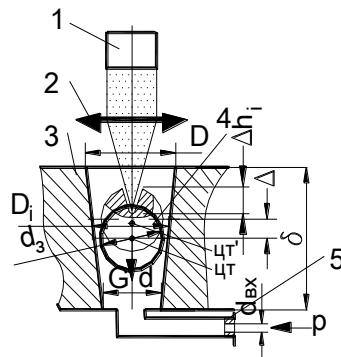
Схема обробки глибоких отворів в заготовці простої форми (кулька, циліндр, диск)
